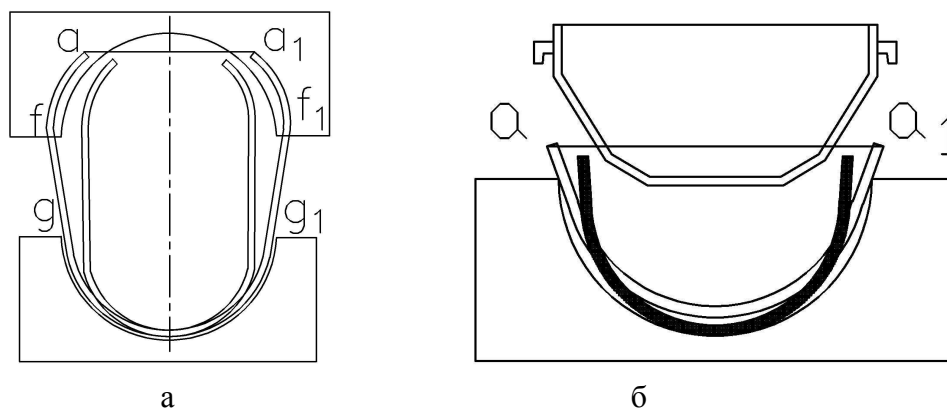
Схема предварительной формовки труб: а – одношовной, б – двухшовной
